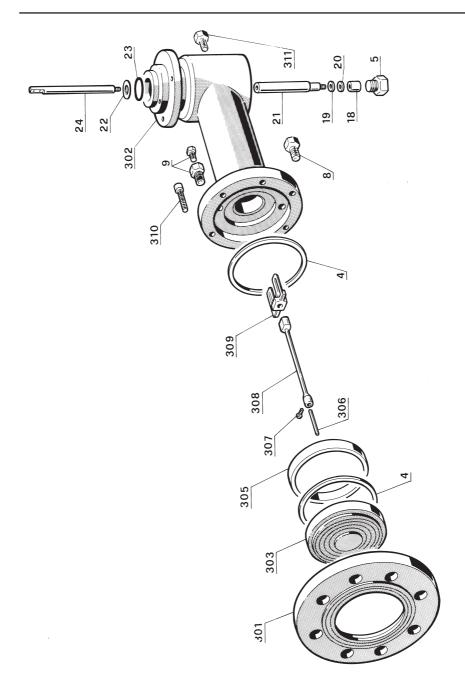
Vista esplosa del relè amplificatore. Exploded view of amplifying relay.
